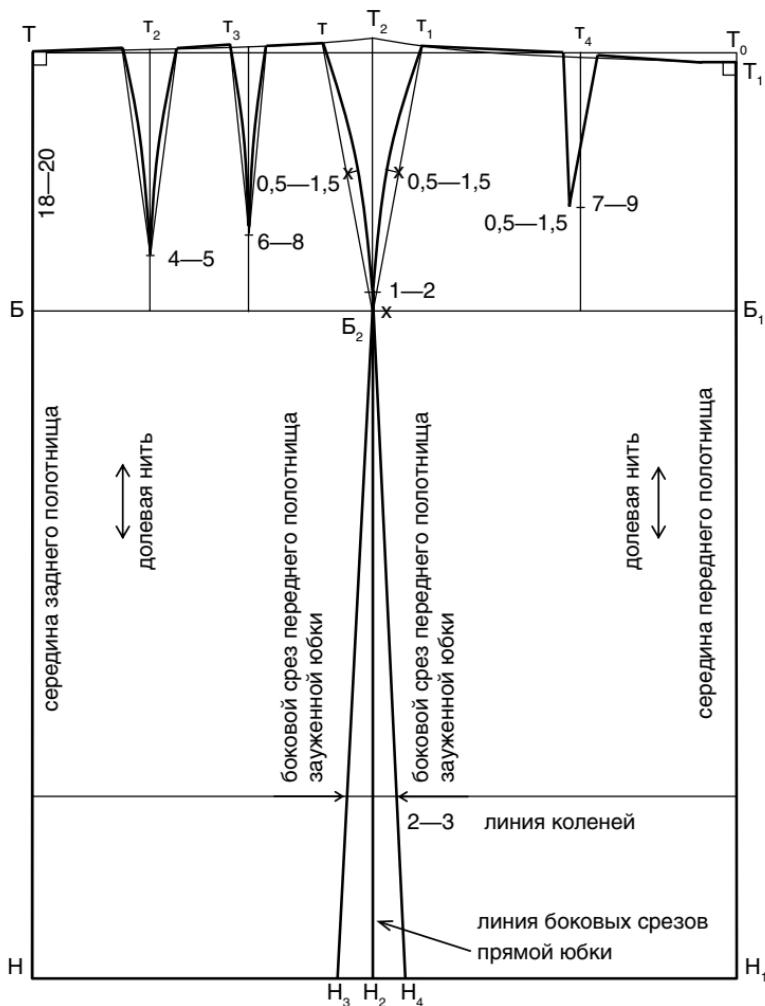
Чертеж конструкции двухшовной юбки с двумя задними вытачками по линии талии
